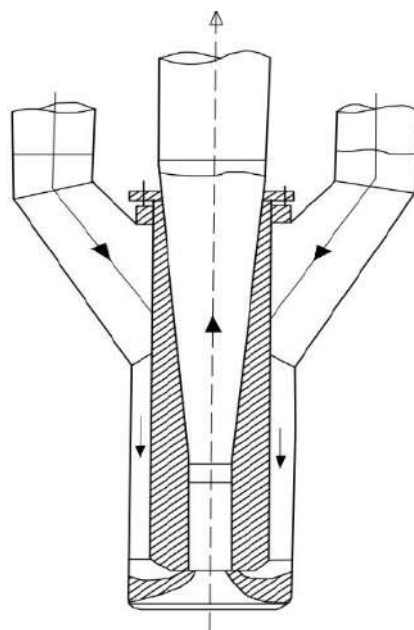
Кольцевой одноповерхностный струйный смеситель
